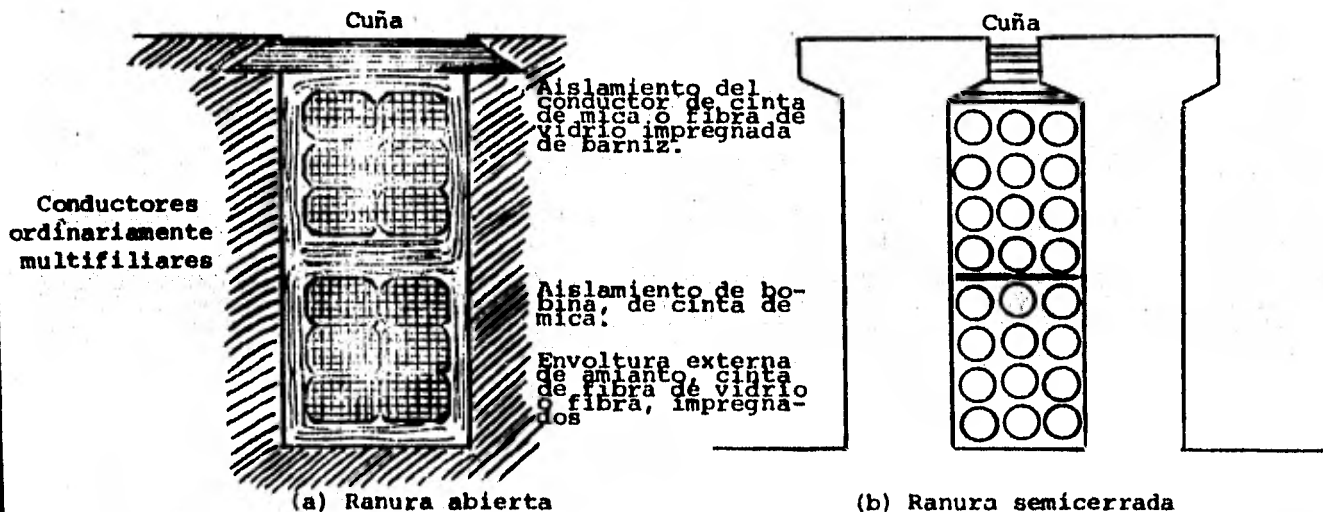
Sección transversal de ranuras típicas para alternadores.
